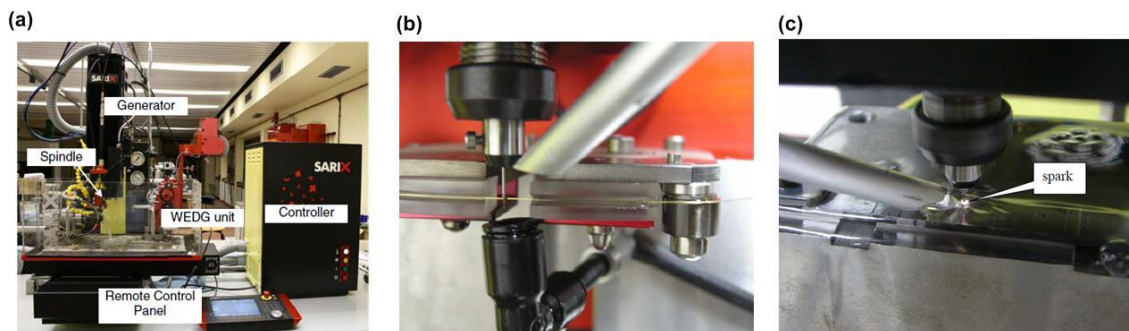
Machine de fraisage par µEE SX-100. (a) Vue d’ensemble d’après [101]. (b) Poste de fabrication des outils par WEDG d’après [100]. (c) Poste de fraisage par µEE d’après [100].
